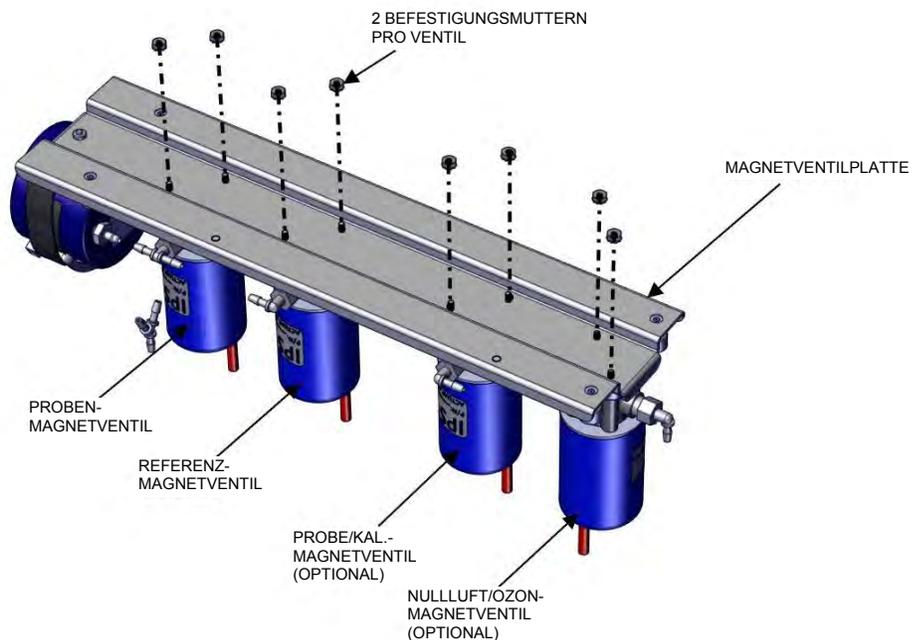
Ausbau der Magnetventilplatte, Teil 2
